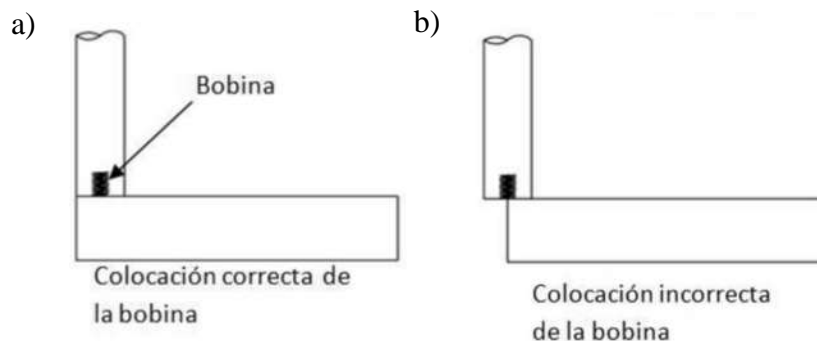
Esquema representativo de la colocación de la bobina a) Posición correcta b) Posición incorrecta [19]
